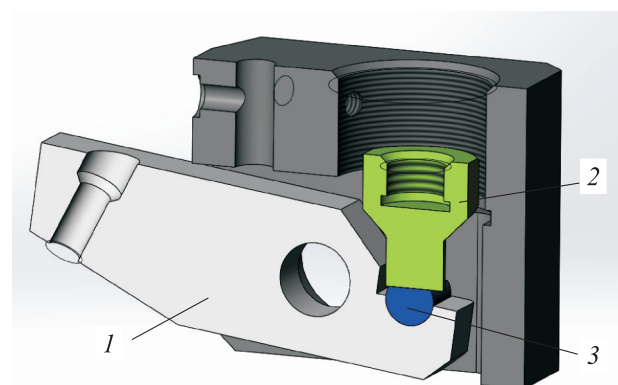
Модель нижнего корпуса СС: 1 — РСХ; 2 и 3 — опора пружины 21 и звено 23 (см рис. 2)
